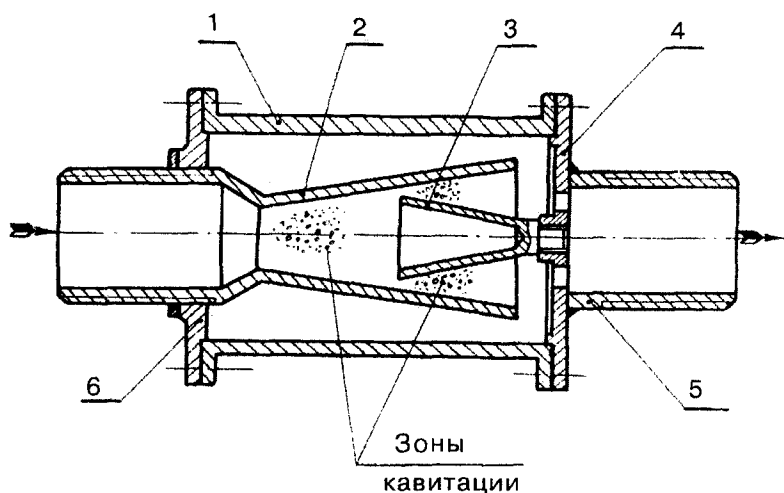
Ультразвуковой диспергатор: 1 – корпус; 2 – сопло; 3 – резонатор; 4, 6 – крышки; 5 – выпускной патрубок
